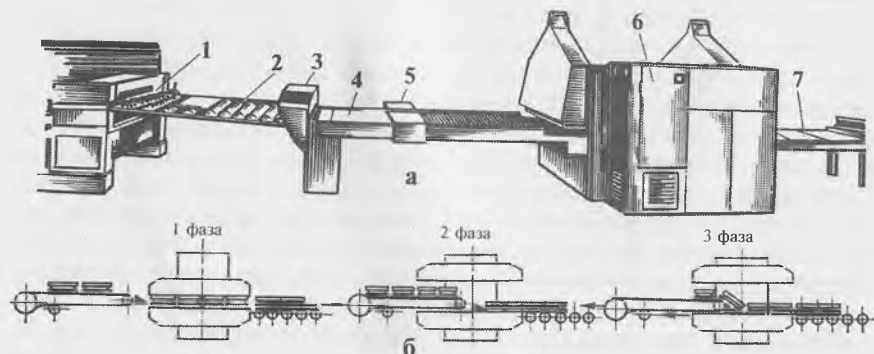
Линия для облицовывания заготовок на базе одноэтажного гидравлического пресса:
